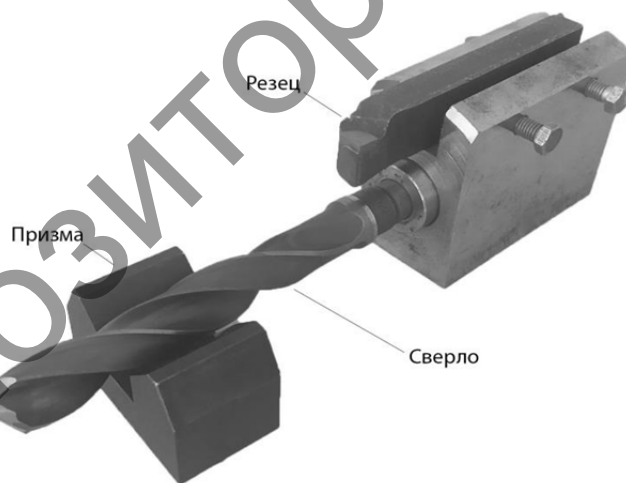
Общий вид приспособления для измерения геометрических параметров режущих инструментов
